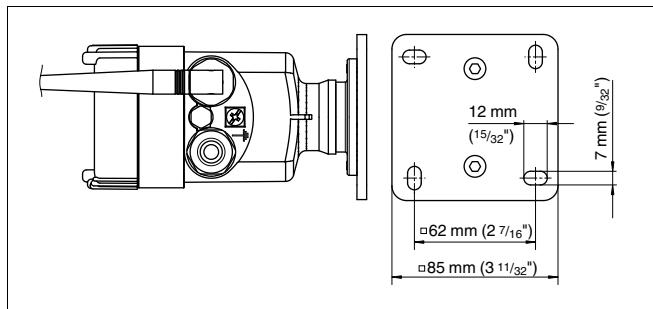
PLICSRADIO D61 для монтажа на стене. Монтажная панель - вид снизу.
